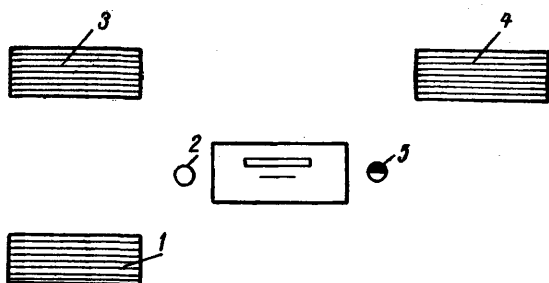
Схема организации рабочего места при работе на круглопильном станке:
